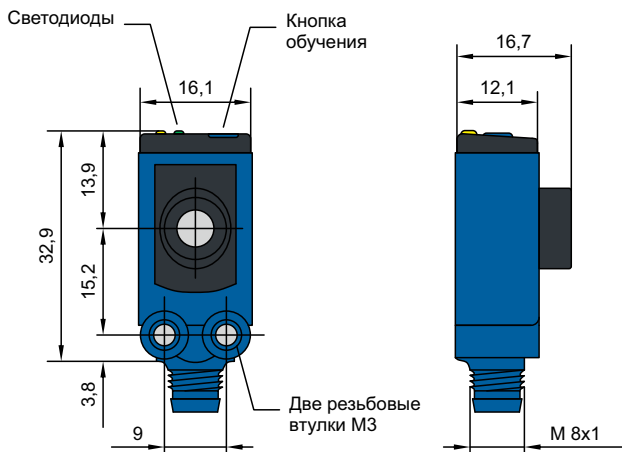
Габаритные размеры датчиков sks-15/...
